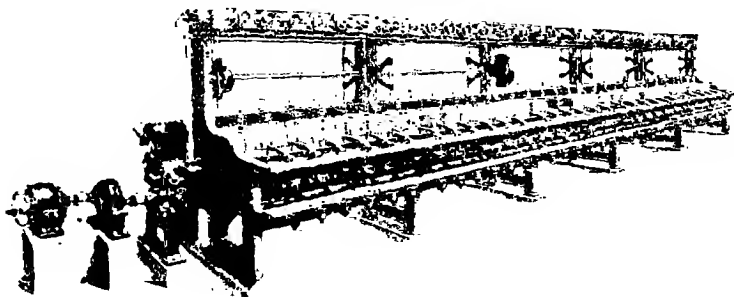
Gesamtansicht der Zentrifugenspinnmaschine der RATINGER MASCHINEN- UND APPARATEBAU A. G.
